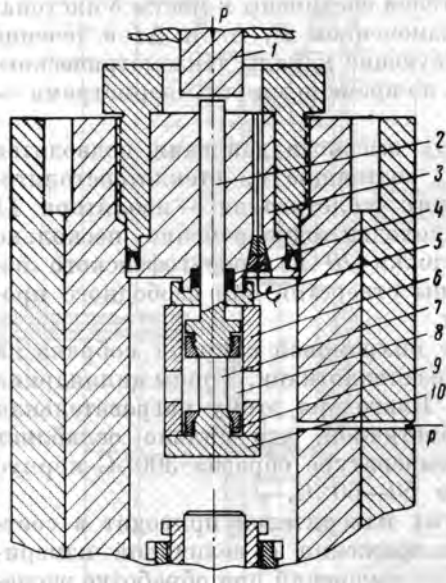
Сборка камеры высокого давления при испытании образцов по второй схеме нагружения.
